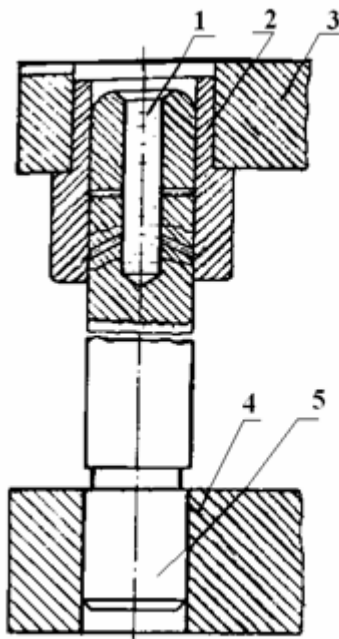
Конструкция направляющих элементов штампа со свободной подачей смазки
